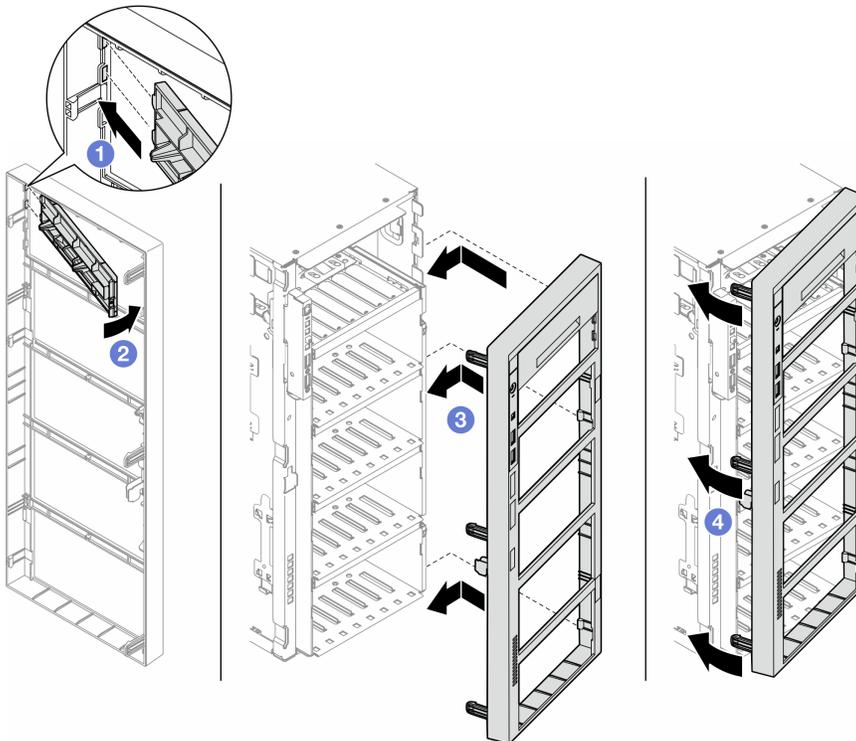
Installation einer Abdeckung der Abdeckblende für eine Laufwerkposition und anschließend einer Frontblende
